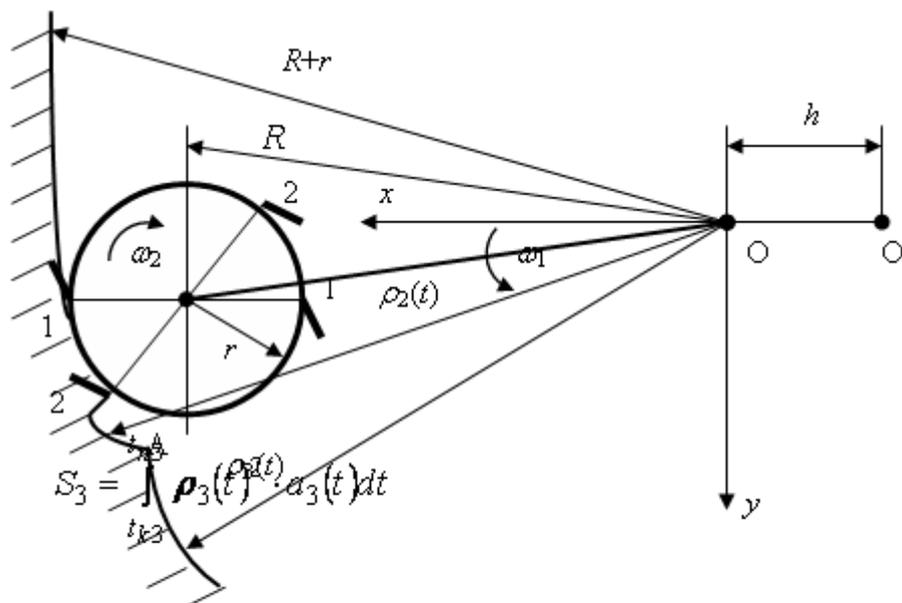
Расчетная схема для качающейся штанги при попутном фрезеровании
